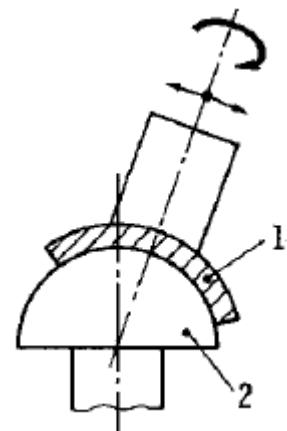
Lapidação de perfil (Klocke 2009)
